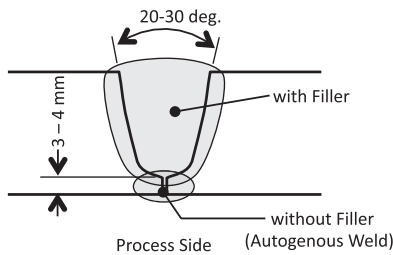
Groove Preparation for But Weld Joint of Cracking Tube
